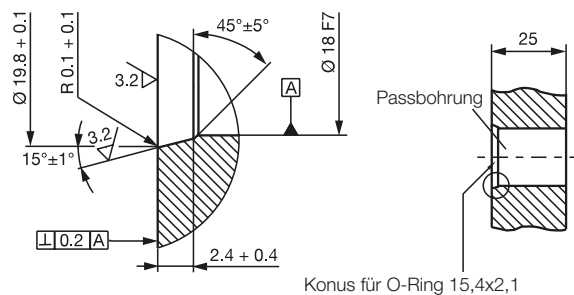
Passbohrung für die Montage des BTL mit O-Ring
